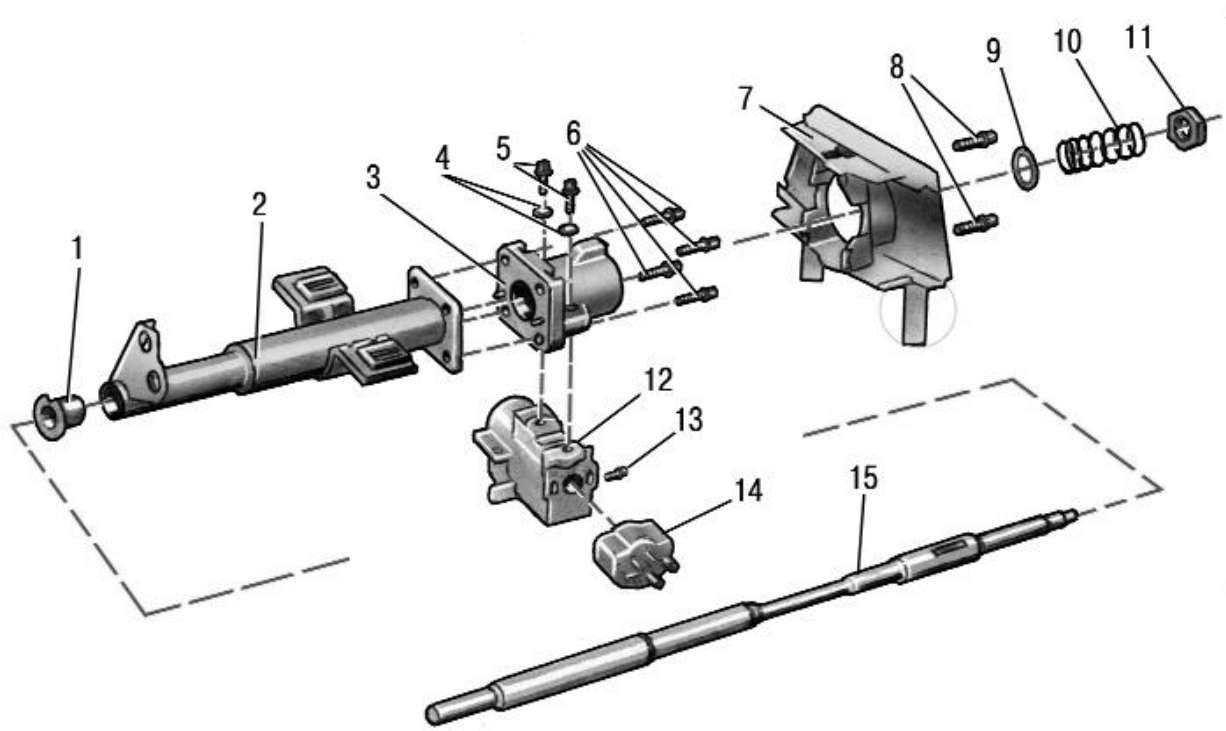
Рульова колонка: 1 – монтажна втулка; 2 – кожух кермової колонки; 3 – верхній корпус кермової колонки; 4 – шайби; 5, 6 – зрізні болти; 7 – корпус кріплення підрульових перемикачів; 8 – гвинти; 9 – завзята шайба; 10 – пружина; 11 – гайка; 12 – корпус кріплення вимикача запалення; 13 - настановний гвинт; 14 – контактна група; 15 – кермовий вал
